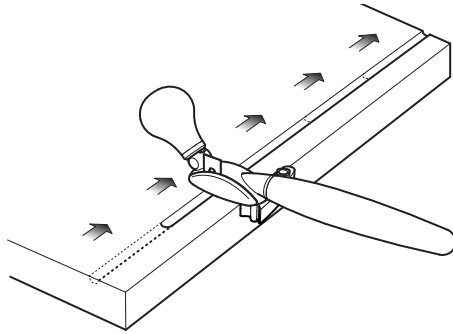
Taille d'une moulure au centre du pied fuselé d'un meuble
